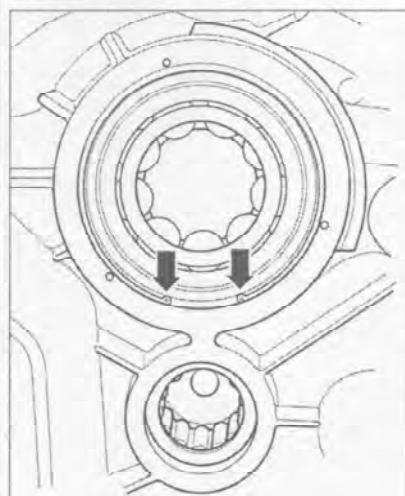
Установите стопорное кольцо так, чтобы его замок был направлен в сторону подшипника вторичного вала.
